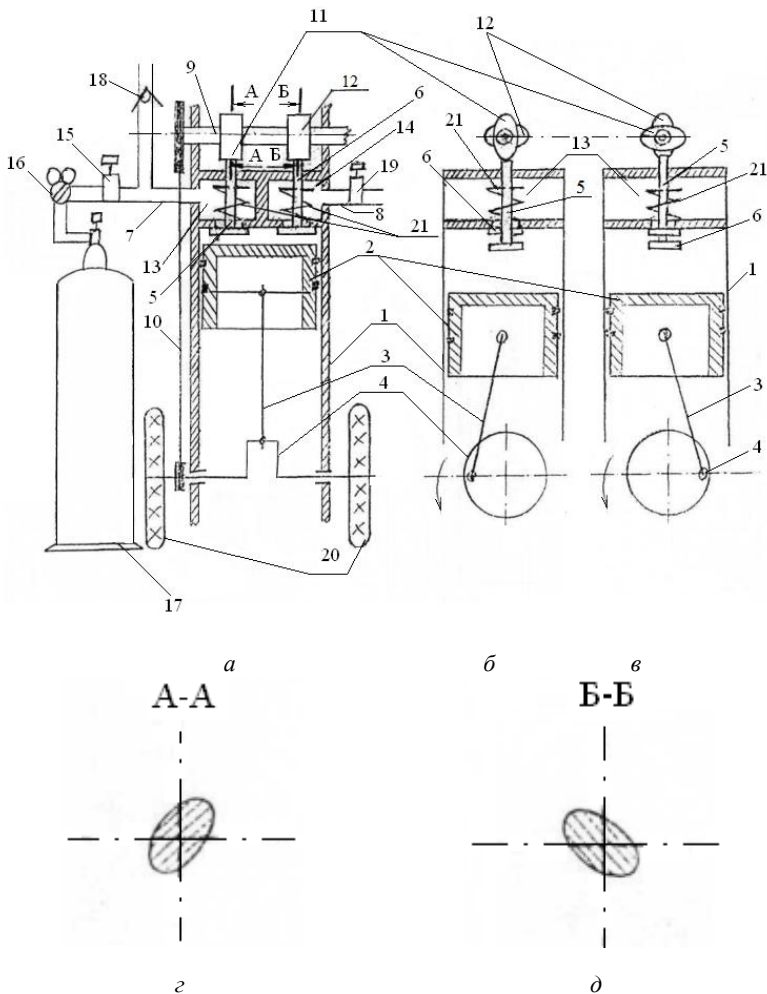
Принципова схема пневматичного двигуна:
